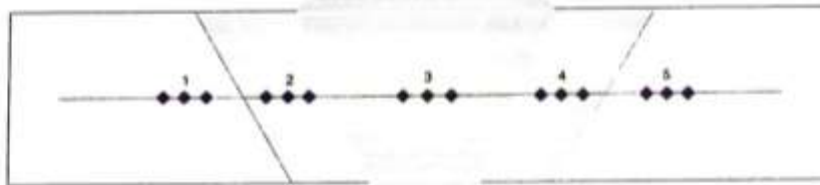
Tabulasi hasil pengujian kekerasan hasil pengelasan SMAW *wet welding* dengan *heat input* sebesar 103,7 kJ/mm
